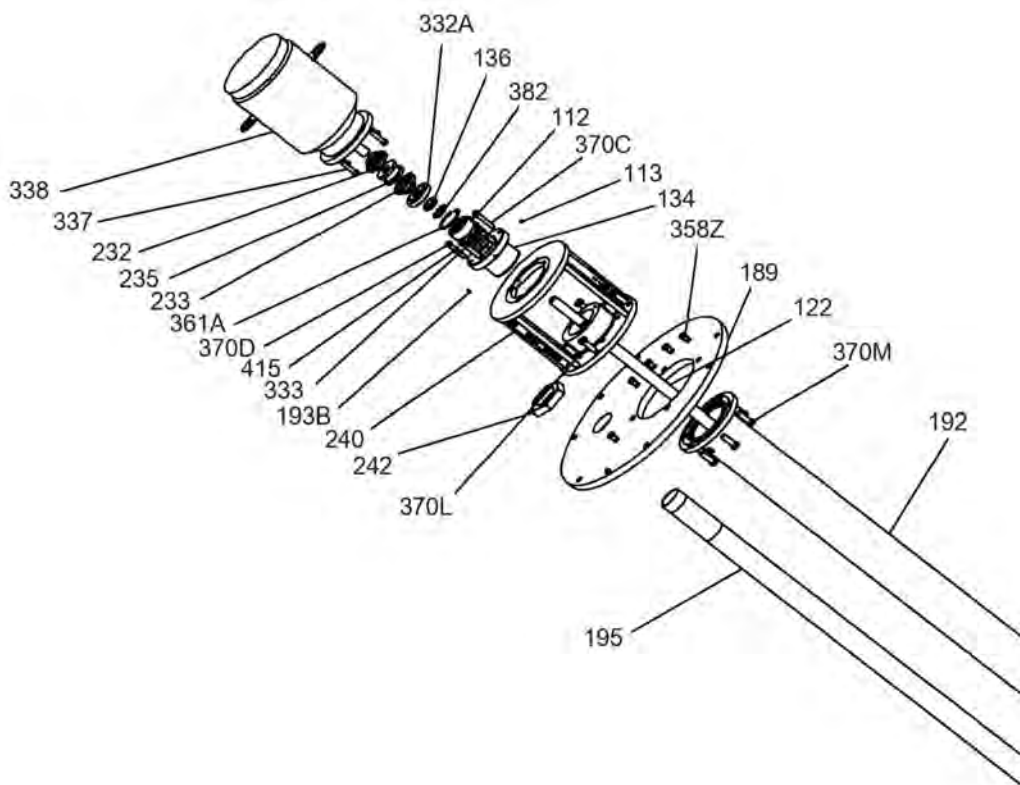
Vue éclatée 3171 (partie 1 sur 2)
